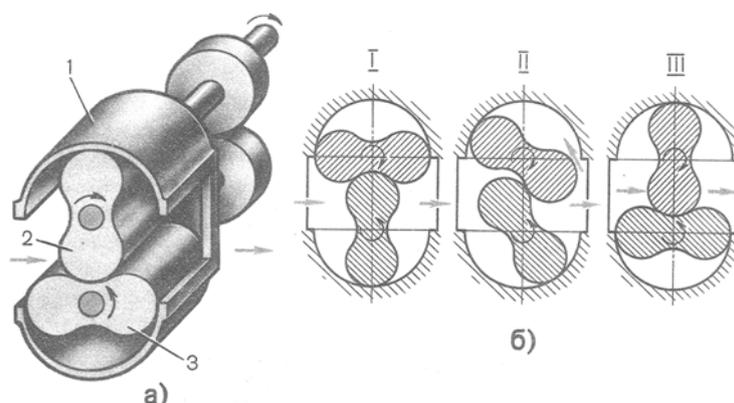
Роторно-шестеренчатый компрессор:
